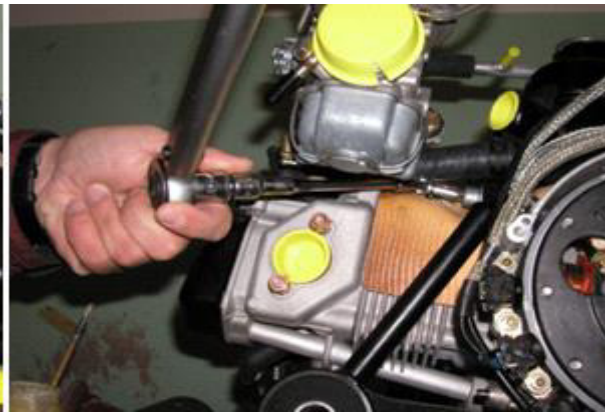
Anziehen der linken Schraube mit Kardangelenk
